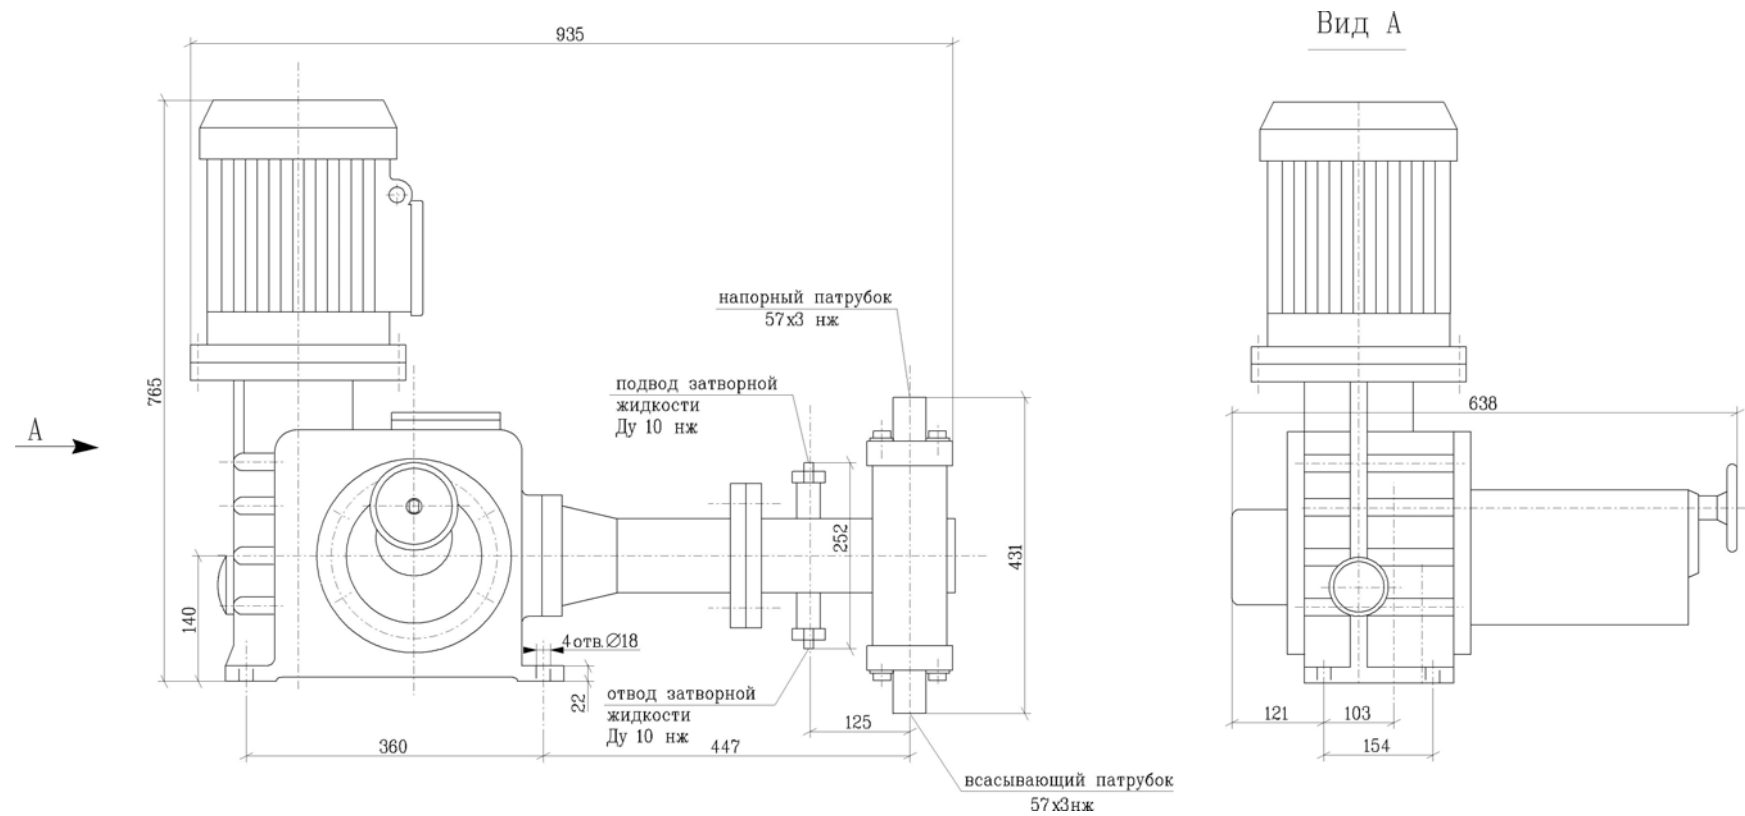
Габаритный чертеж насоса-дозатора щелочи LDP20AP001, LDP20AP002
